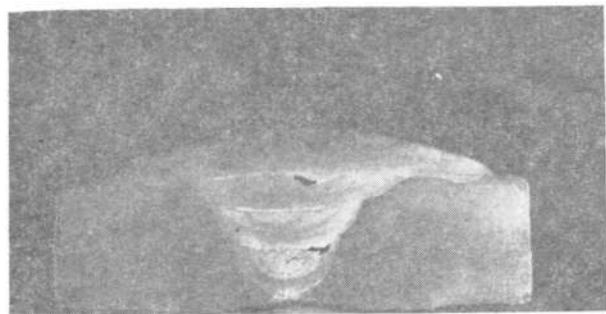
Несплавление металла между валиками при сварке плавящимся электродом.
